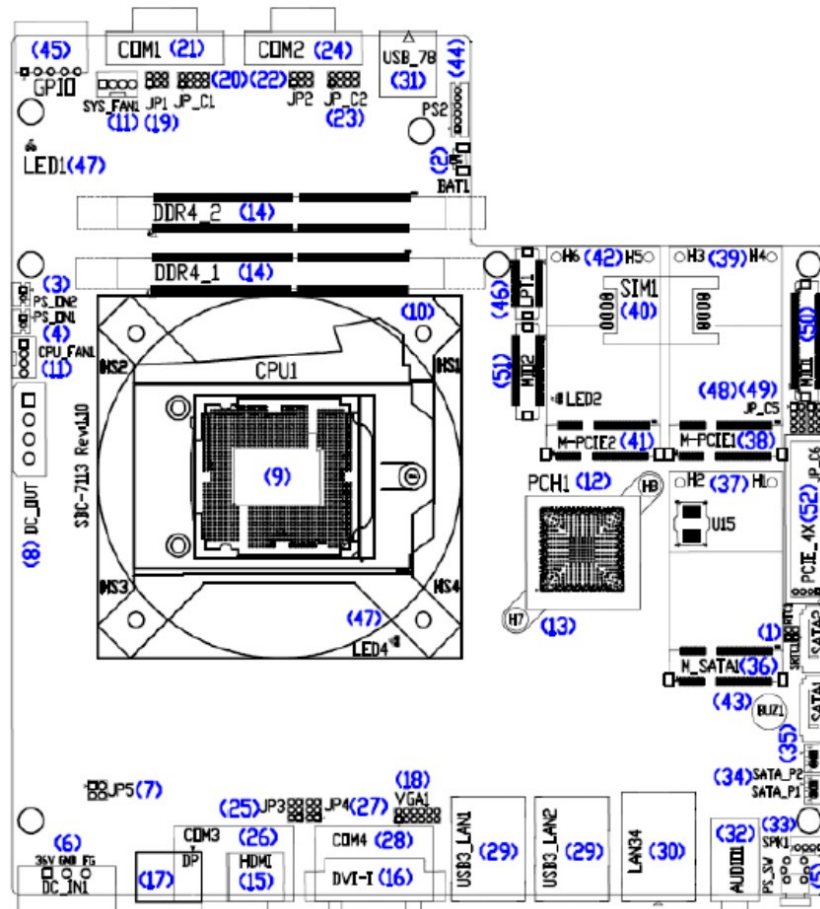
SBC-7113 - Anschlüsse und Jumper - Draufsicht
